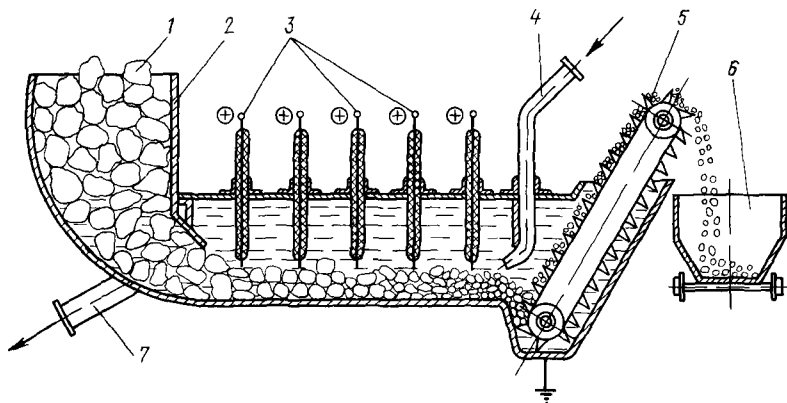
19 Электрогидравлическое устройство для непрерывного выделения металла из шлаков
